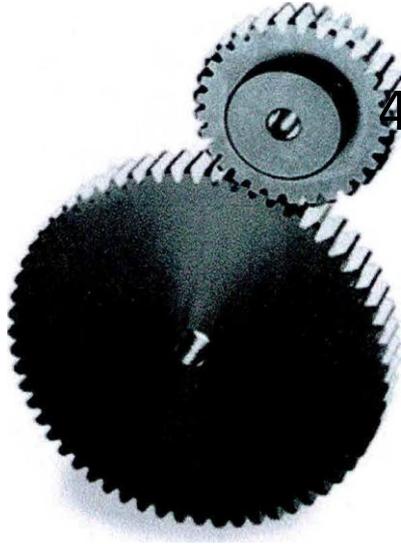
Engrenage pour augmenter la vitesse de rotation.
